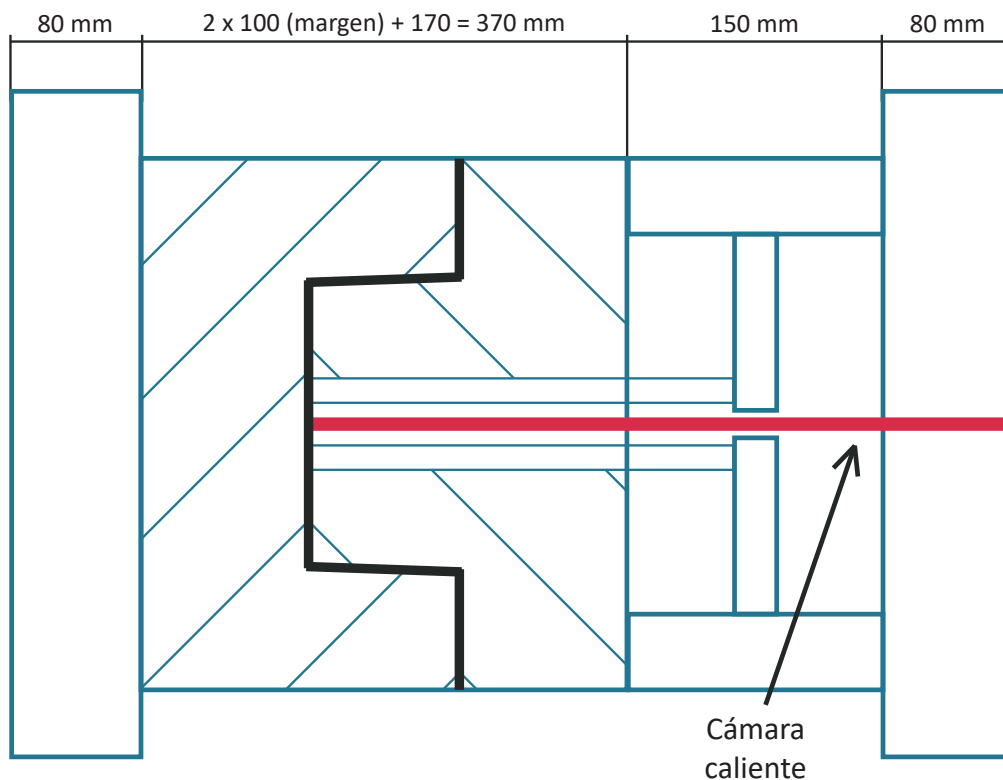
Molde de la tapa que muestra el espesor mínimo de molde
